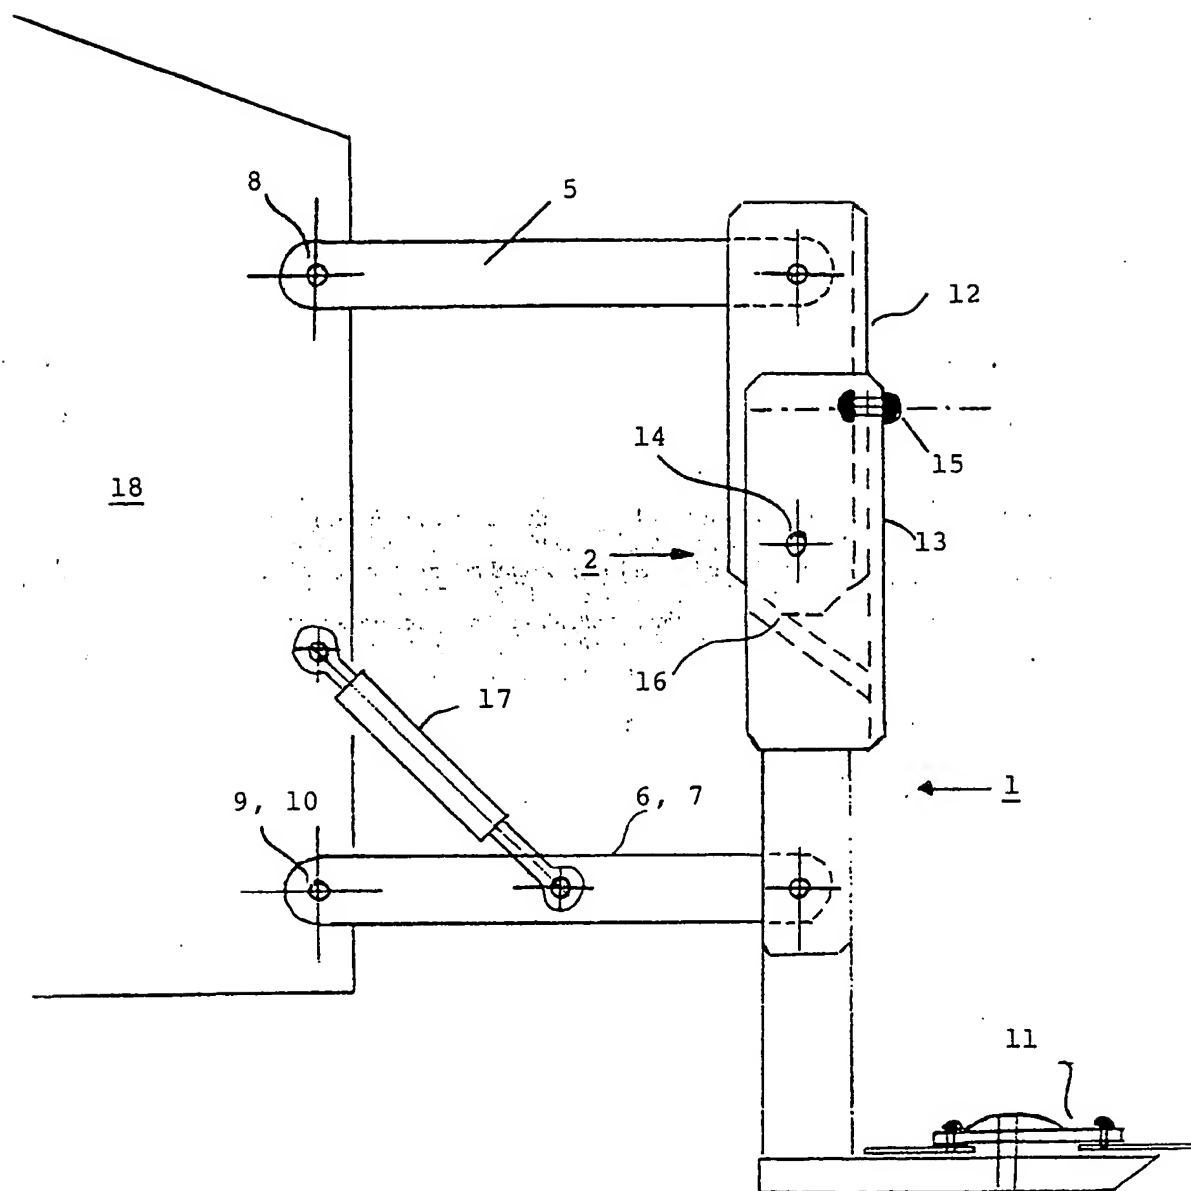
Teile des Gelenkscharniers im Grundriss.
